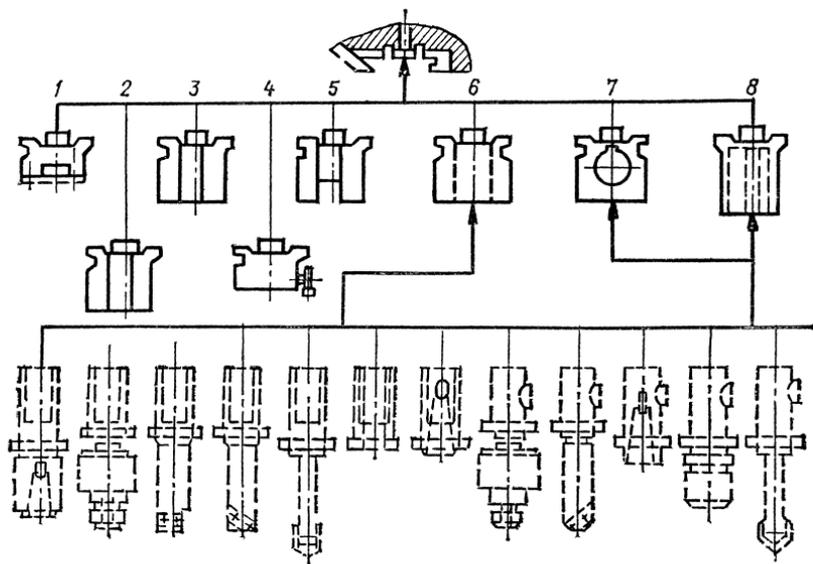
Подсистема вспомогательного инструмента с базирующей призмой для станков с ЧПУ токарной группы
